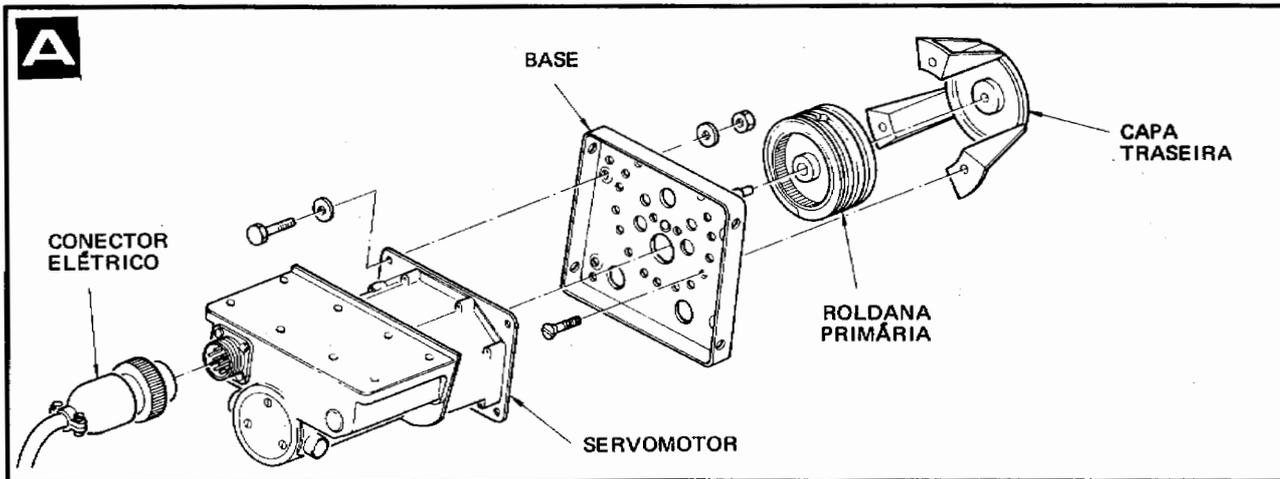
Instalação da Roldana Primária do Profundor e do Leme de Direção
